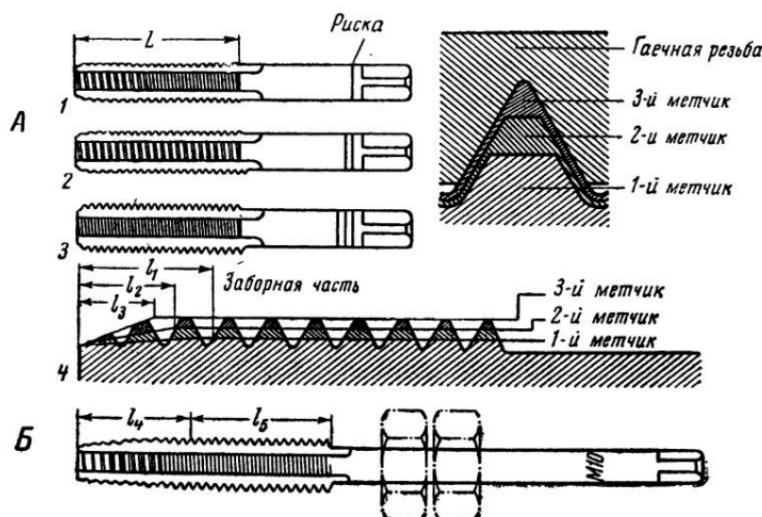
Метчики: А — ручные (1 — первый черновой, 2 — второй черновой, 3 — третий чистовой, 4 — профиль резьбы метчиков); Б — машинный гаечный метчик.
